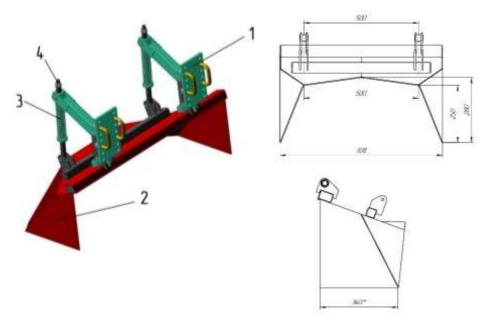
Гребнеобразователь с подвесом (вариант поставки) 1 — кронштейн; 2 — гребнеобразователь; 3 — предохранительный механизм; 4 — гайка прижимная.
